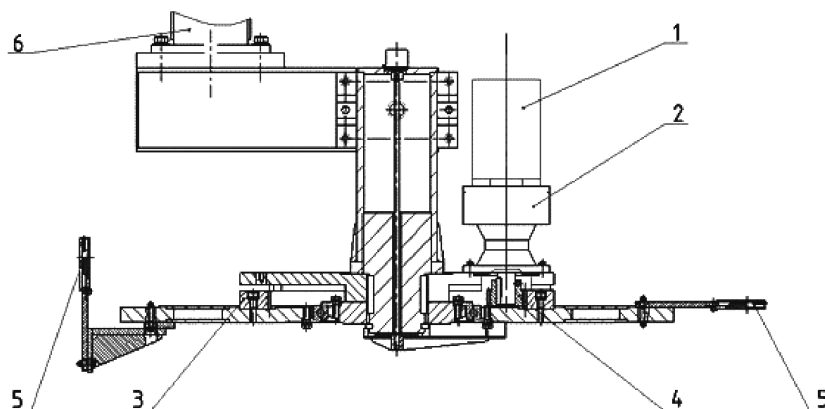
Магазин инструментов на 28 посадочных гнезд под различный инструмент:
